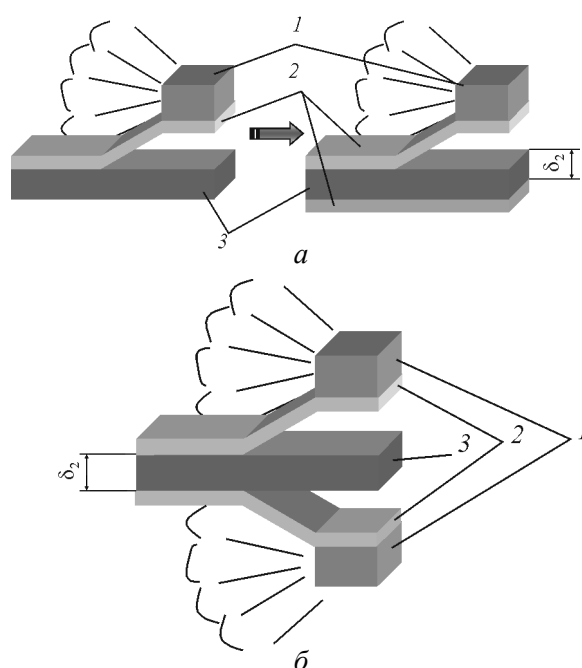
Принципиальные схемы сварки взрывом трехслойного композита с двусторонней симметричной плакировкой: *a* — последовательное плакирование противоположных поверхностей материала основы; *б* — одновременное плакирование (батарейная схема); 1 — заряд взрывчатого вещества (ВВ); 2 — плакирующая пластина; 3 — плакируемая пластина (основа)
